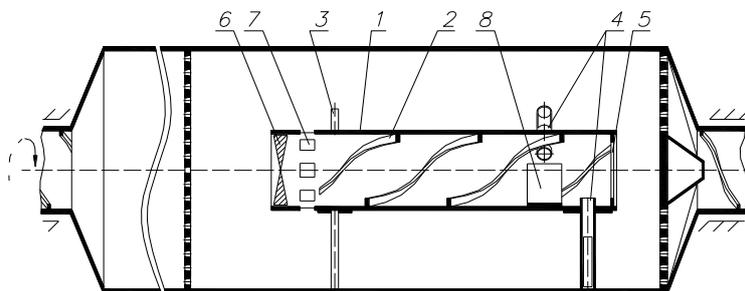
Схема трубной мельницы с внутримельничным устройством: 1 – барабана; 2 – транспортирующие лопасти; 3 – стойки; 4 – лифтеры; 5 – подпорное кольцо; 6 – вентиляторное колесо; 7 – отверстия; 8 – защитные элементы
